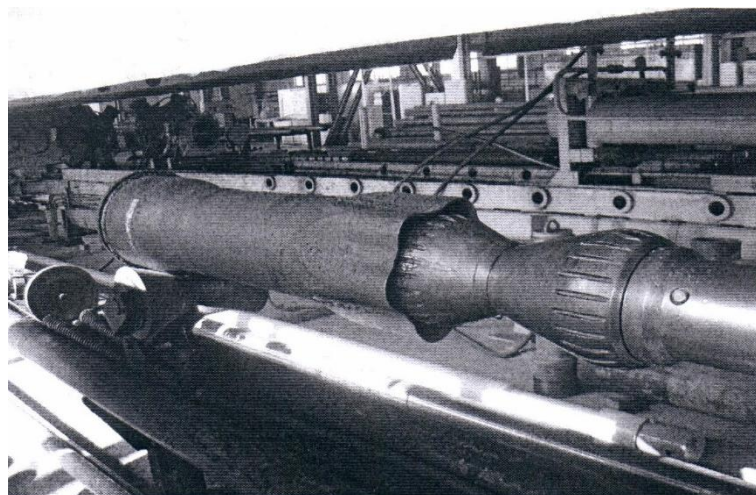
Схемы гидравлических испытаний посадочного устройства
